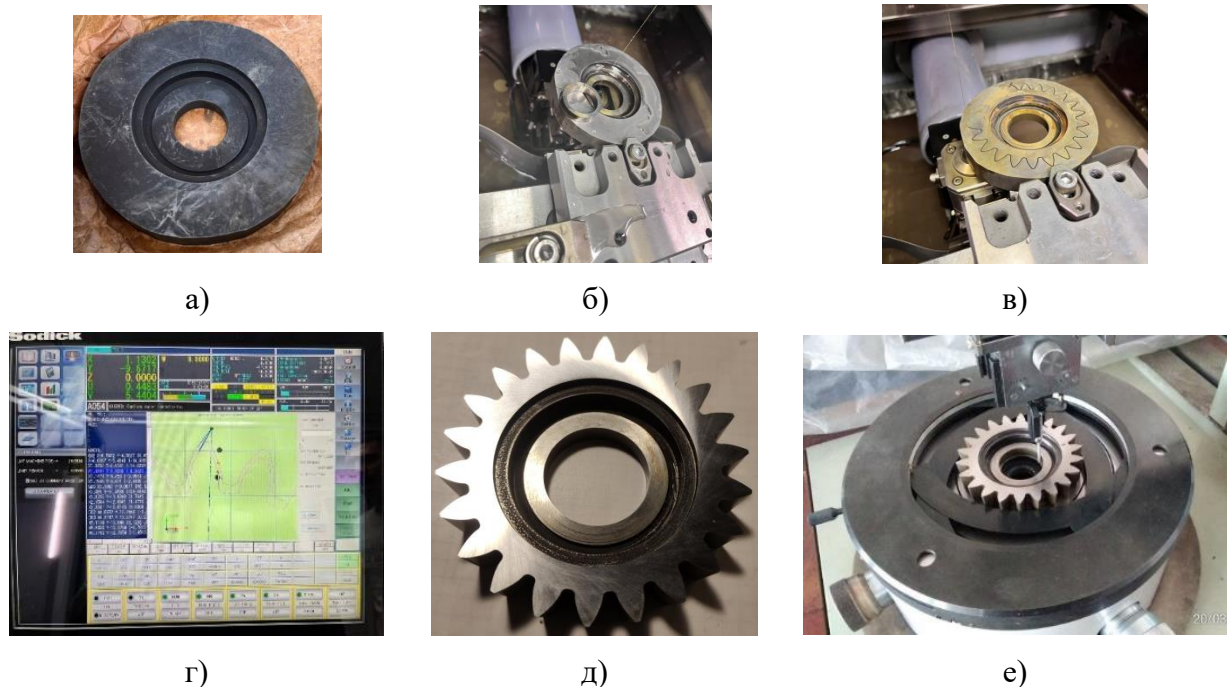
Виготовлення дискового довбача: а) заготовка; б) вирізання посадкового отвору; в) вирізання задньої вершинної та бічної поверхні довбача; г) стійка верстата з керуючою програмою; д) виготовлений довбач; е) вимірювання параметрів довбача
